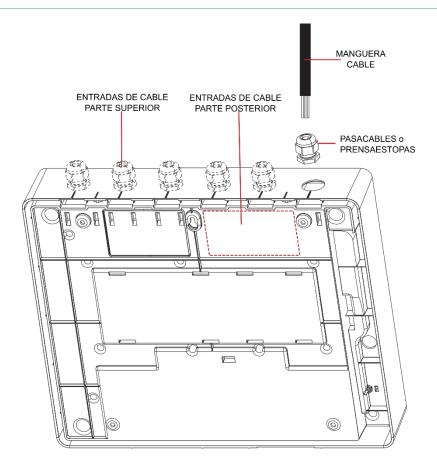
Zonas previstas para entrada de cable en parte trasera y superior.
